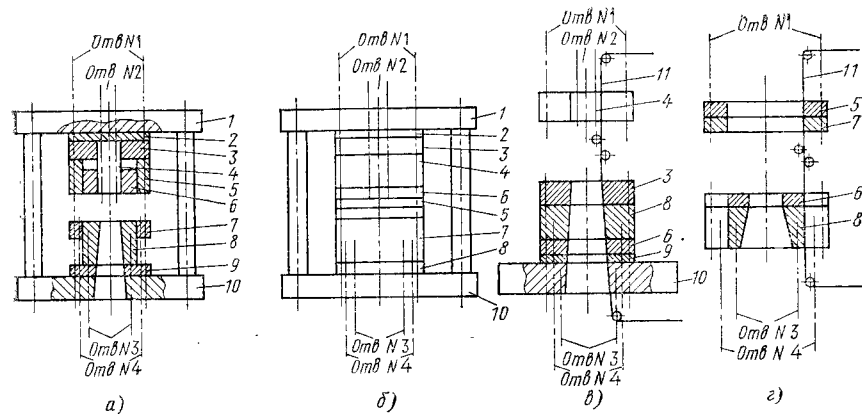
Вырубной штамп совмещенного действия (а), сборка заготовок его основных деталей (б) и схемы их обработки (в, г)
